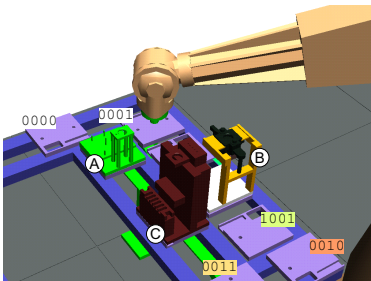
Optimierung einer Werkzeugposition in der Laserbearbeitung
